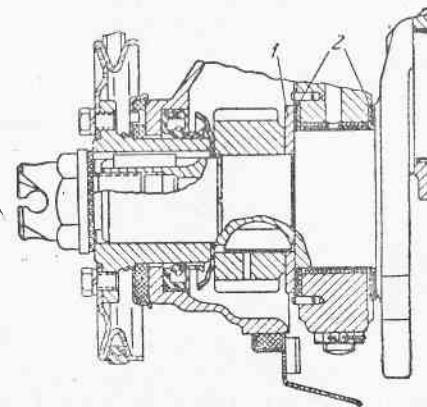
Передний конец коленчатого вала двигателя М-21 «Волга».
